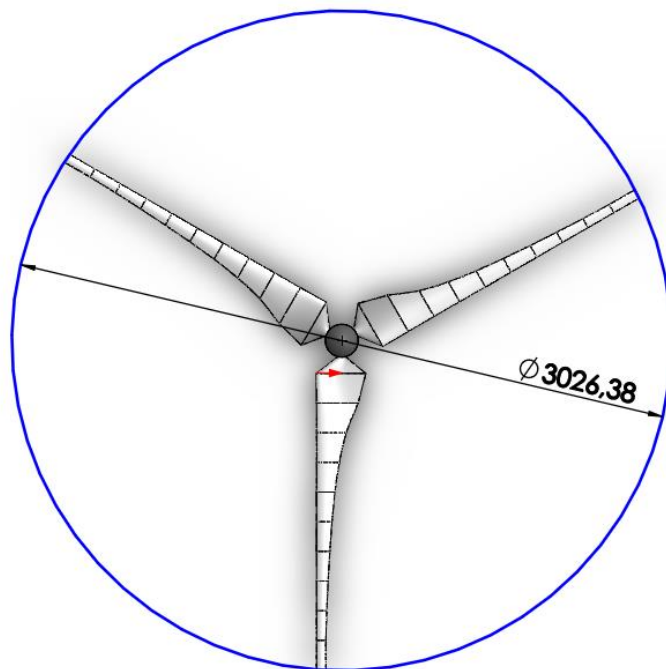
Vista isométrica do rotor, com destaque para o ângulo de pitch das pás.
